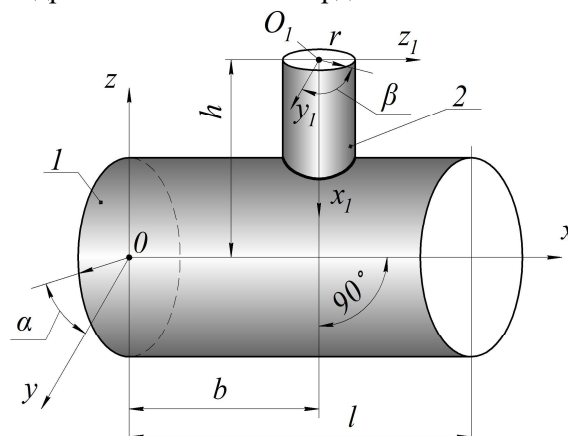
Схема пересечения двух цилиндрических поверхностей: поверхности корпуса 1 и поверхности штуцера 2
